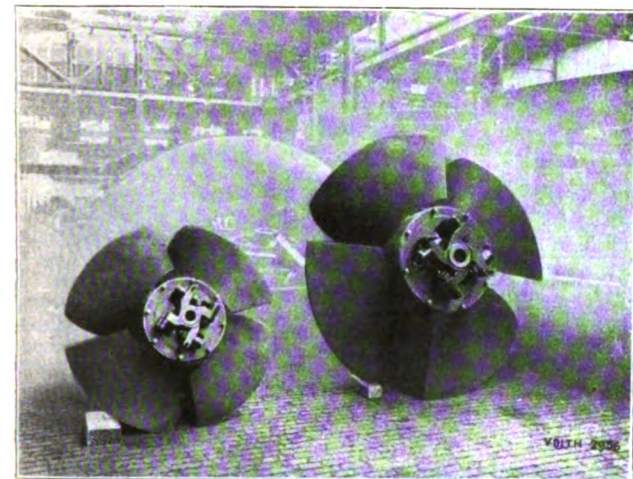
Kaplanlaufräder für hohes Gefälle mit langen Schaufeln.
